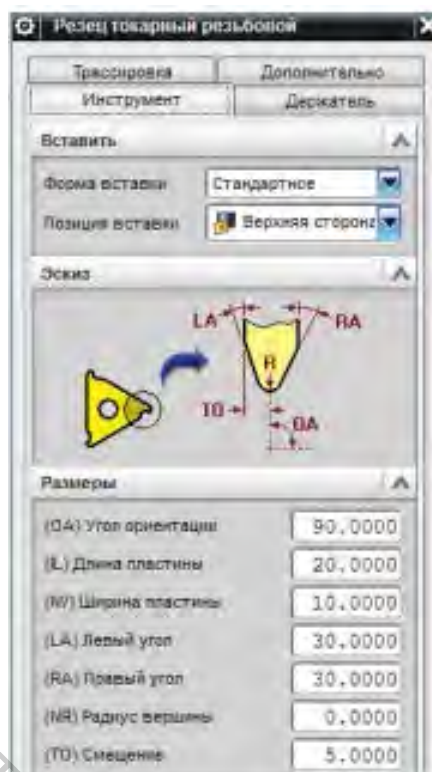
Выбор геометрии и размеров режущей пластины резьбового резца
